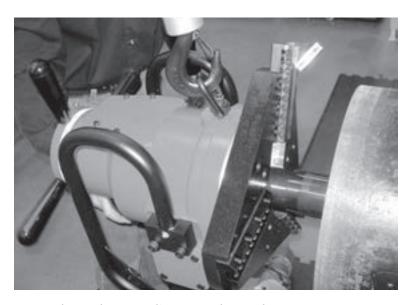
Poussez la machine vers l'avant sur le mandrin.
